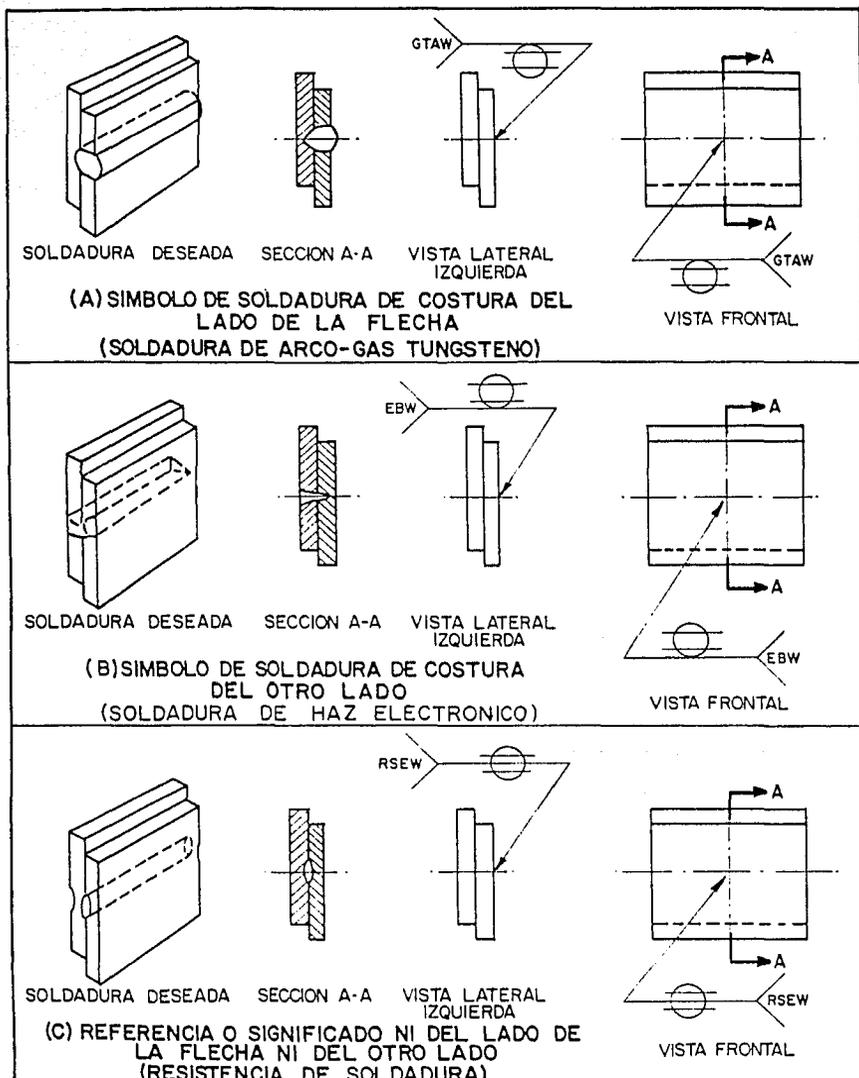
APLICACION DEL SIMBOLO DE SOLDADURA DE COSTURA
